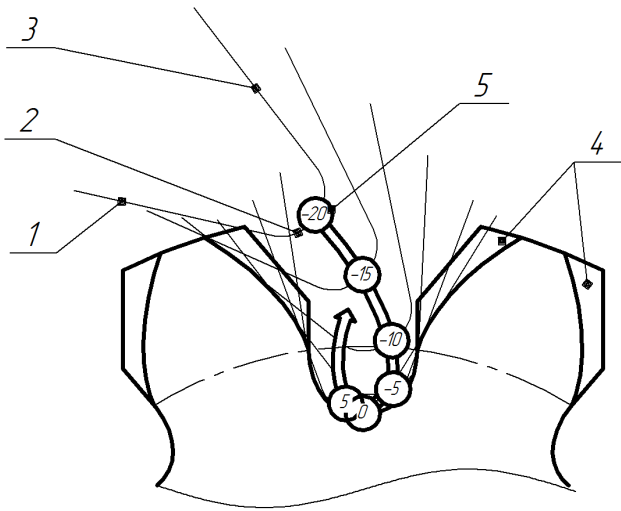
Схема розташування твірних позицій зубця черв'ячної фрези при традиційному чистовому зубофрезеруванні
